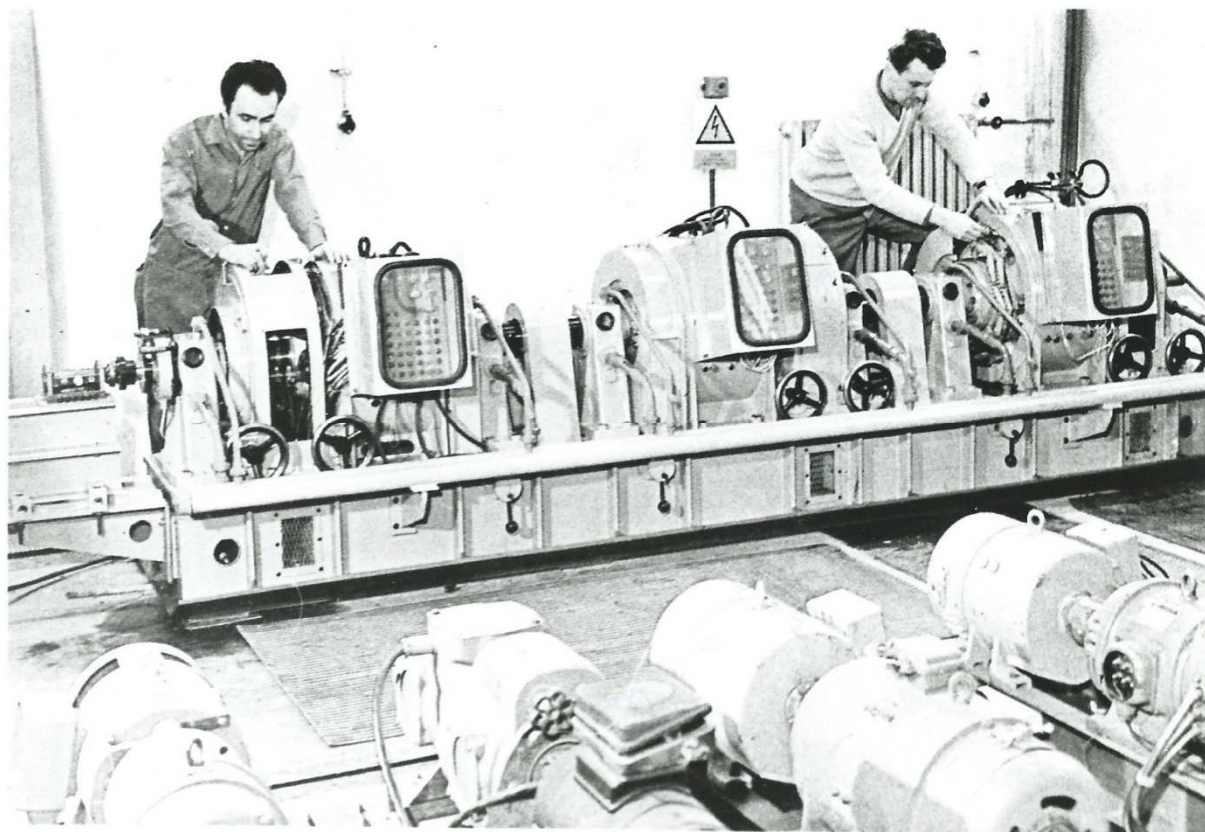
Stejnoseměrný trakční motor TM 3928/4 pro motorový vůz M 262
